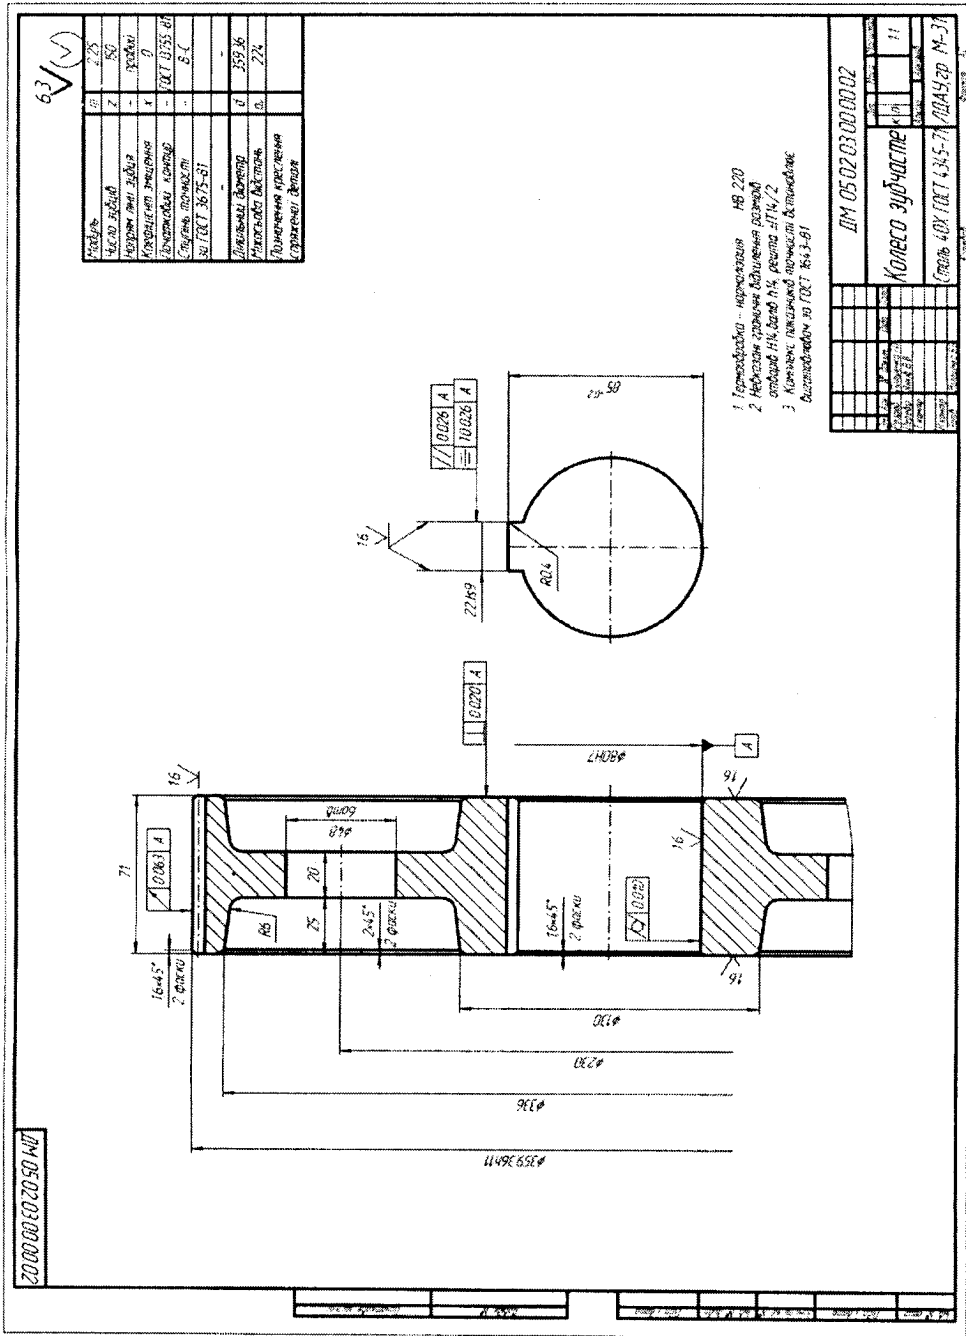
Пример рабочего чертежа цилиндрического зубчатого колеса
